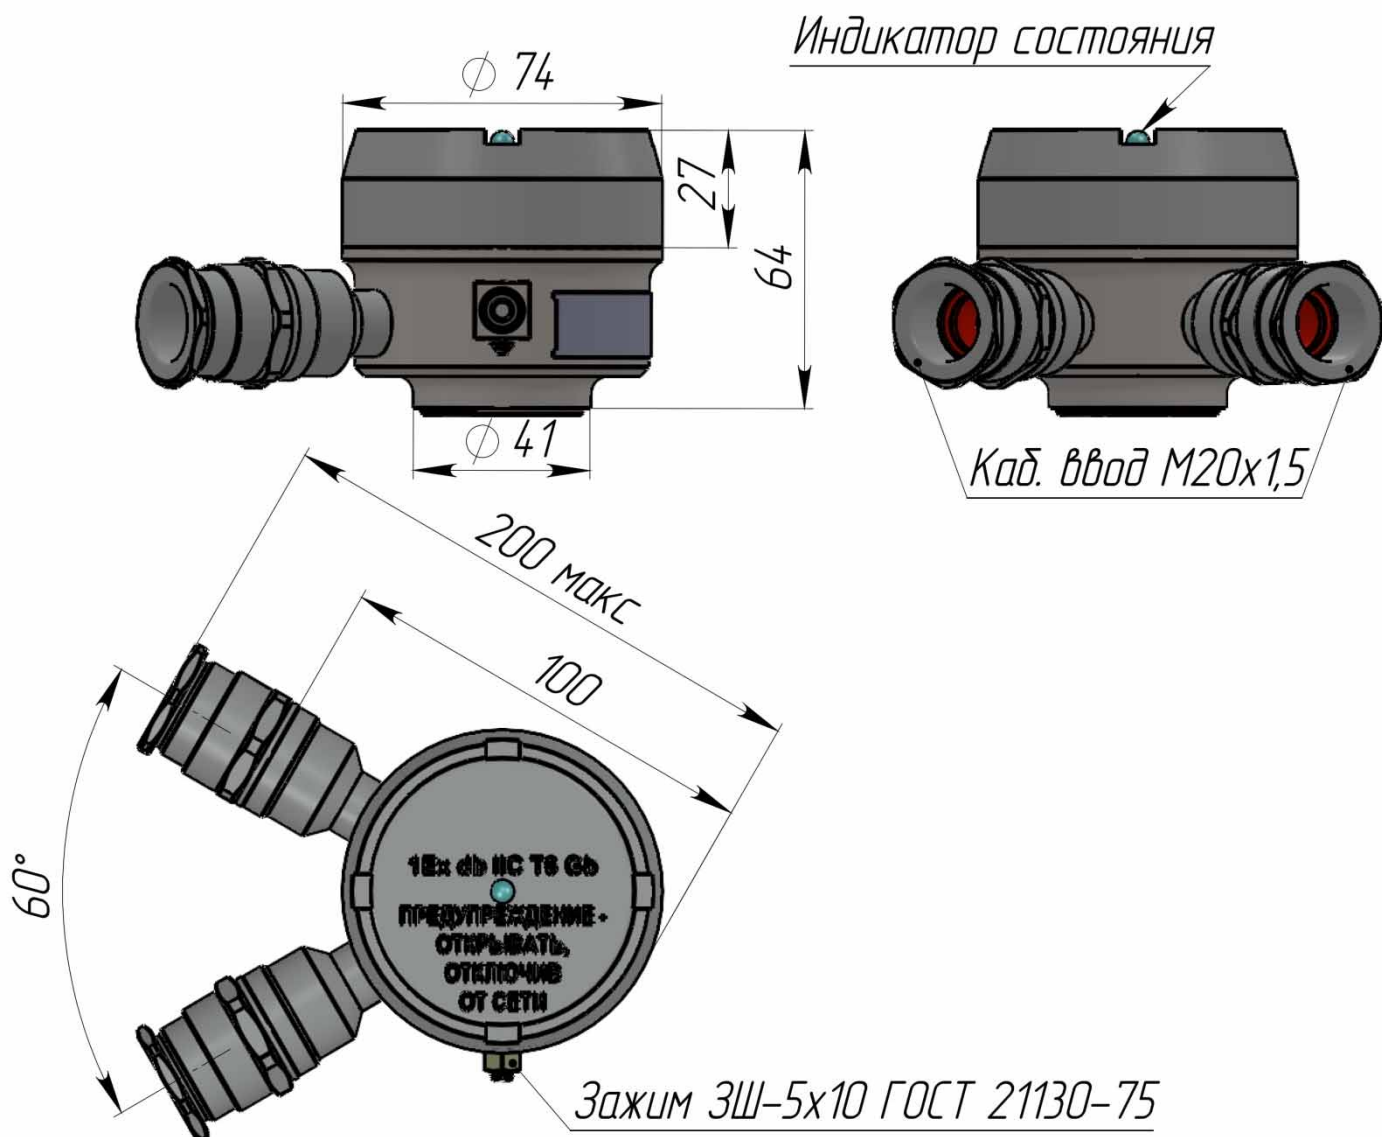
Габаритные размеры корпуса блока электронного в корпусе из нержавеющей стали для оборудования класса безопасности ЗН (два кабельных ввода)
